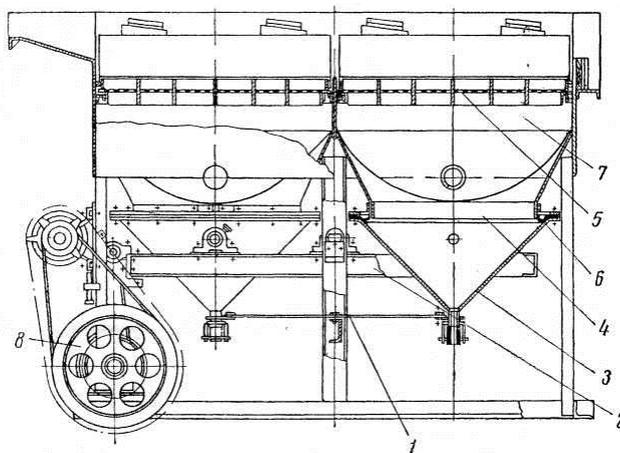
Диафрагмовая отсадочная машина МОД-2: 1- пружина; 2 – рама – коромысло; 3 – подвижное коническое днище; 4 - цилиндрическая обечайка; 5 – решетка; 6 - резиновые манжеты; 7 – корпус; 8- кривошипно-шатунный механизм
